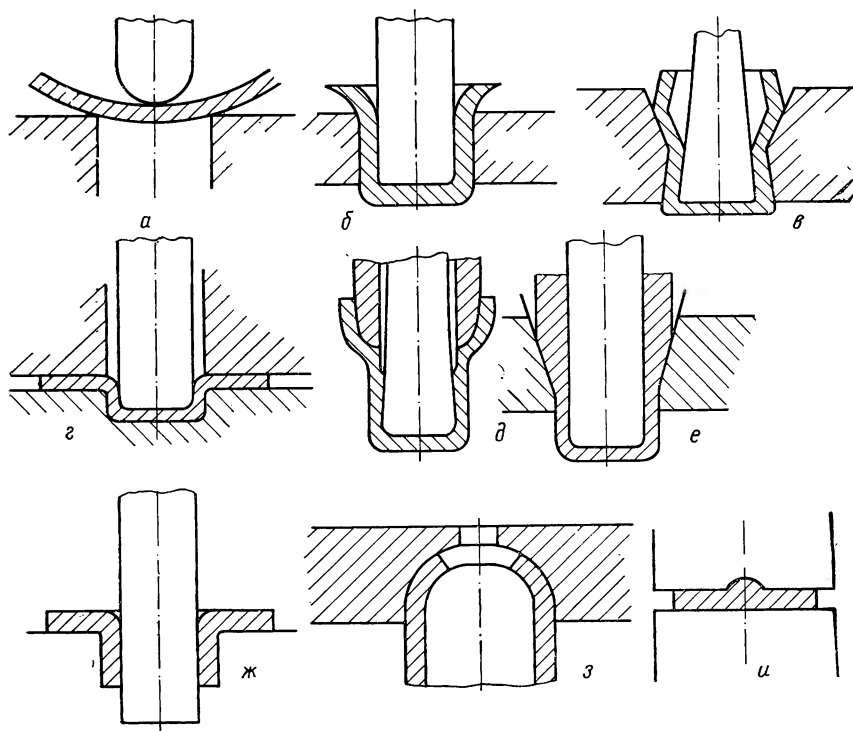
Операции листовой штамповки, связанные с прессованием:
